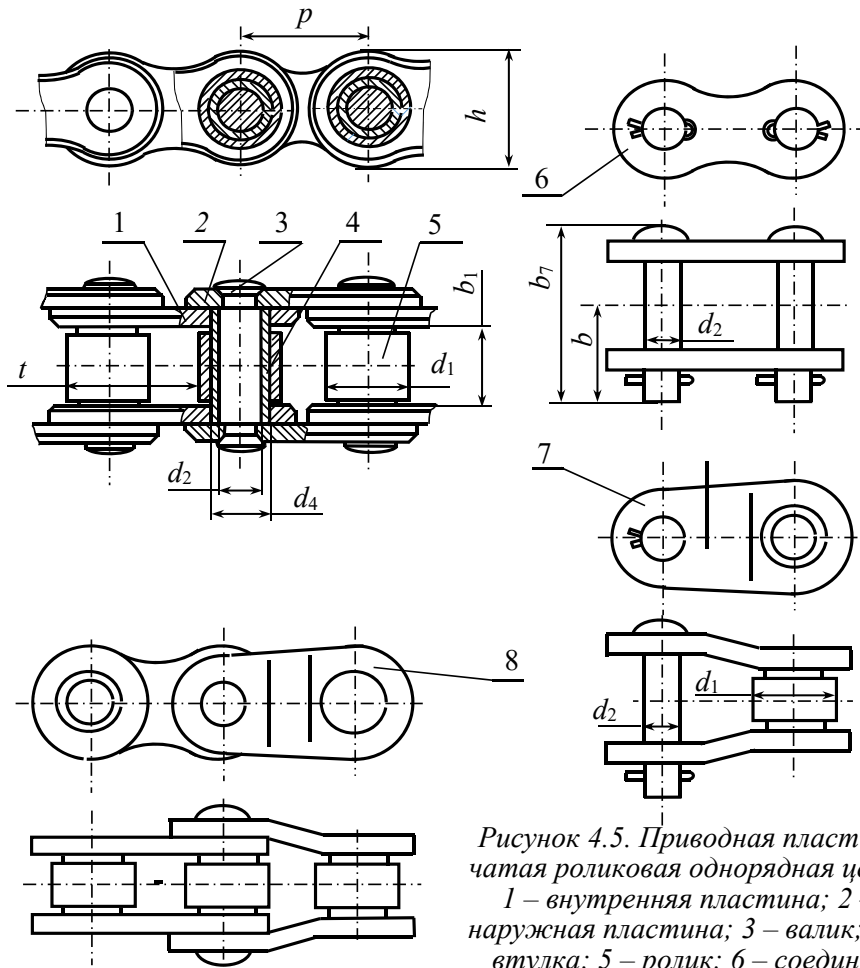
Приводная пластинчатая роликовая однорядная цепь: 1 – внутренняя пластина; 2 – наружная пластина; 3 – валик; 4 – втулка; 5 – ролик; 6 – соединительное звено; 7 – переходное
